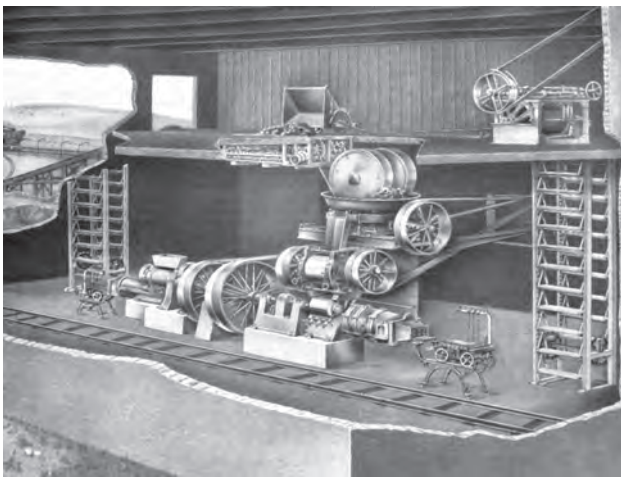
Aufbereitungsanlage mit Kastenbeschicker, Kollergang, Walzwerk, Strangpresse, um 1920
